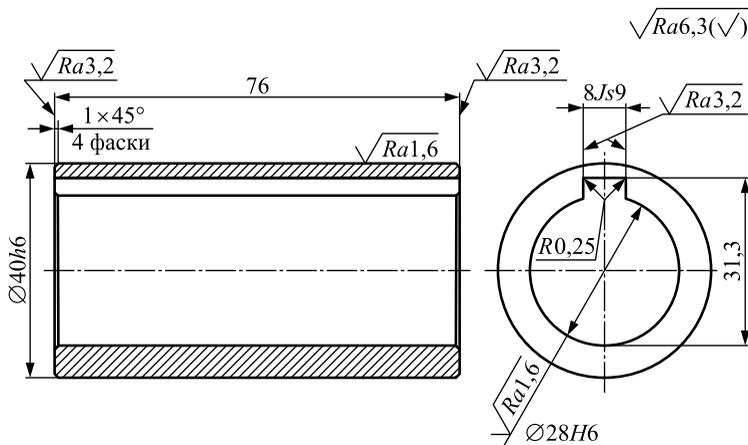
Обозначение шероховатости поверхностей (пример 2)
